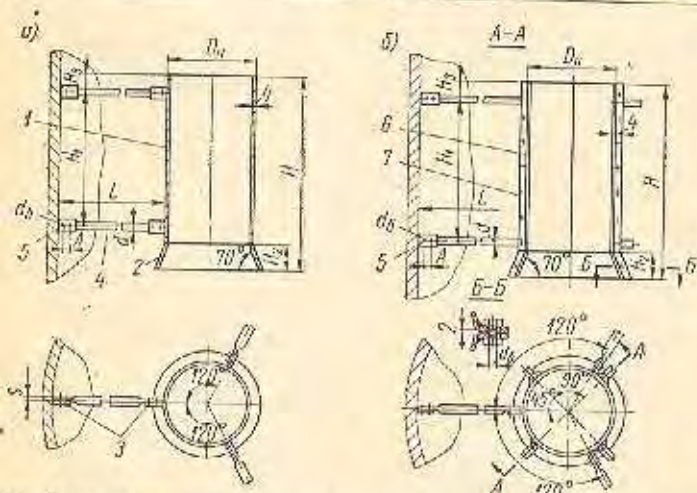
Конструкции направляющей трубы для пропеллерных переменивающих устройств по МН 5874—66: а — неразъемная (цельная) направляющая труба, шифр 73; б — разъемная направляющая труба, шифр 74; 1 — труба; 2 — конус; 3 — ушко; 4 — тяга; 5 — болты, гайки и шайбы; 6 — труба из четырех частей; 7 — планки для соединения четырех частей трубы между собой
